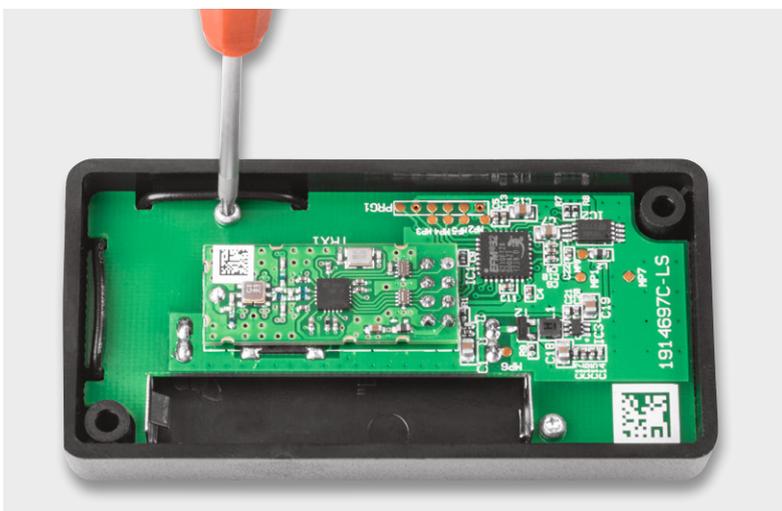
wird mit zwei Schrauben im Gehäuse fixiert.
